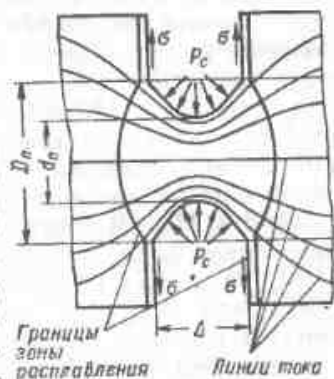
Схема перемычки расплавленного металла при сварке оплавлением
